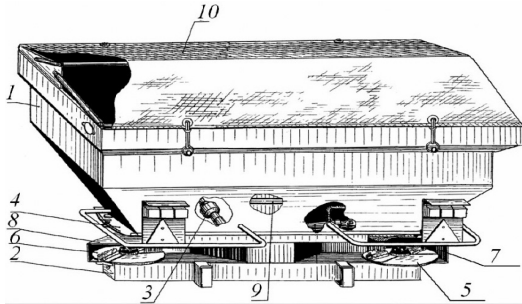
Общий вид бункерного навесного рассеивателя твердых минеральных удобрений: 1 – бункер; 2 – механизм привода; 3 – карданная передача; 4 – левое дозирующее устройство; 5 – правый дисковый метатель; 6 – левый дисковый метатель; 7 – правый отражатель; 8 – левый отражатель; 9 – рыхлитель; 10 – тент
